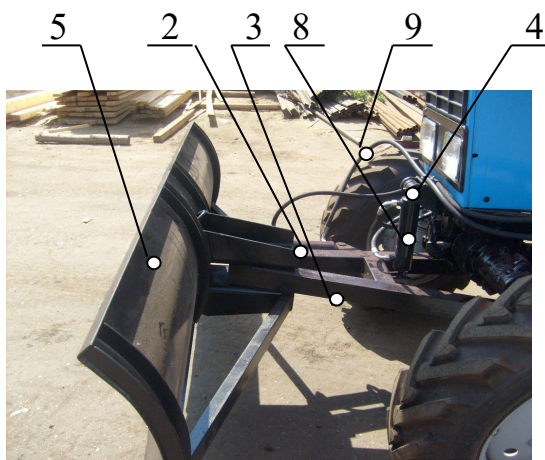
Сборка Рамы, Лопаты, установка гидроцилиндров.
